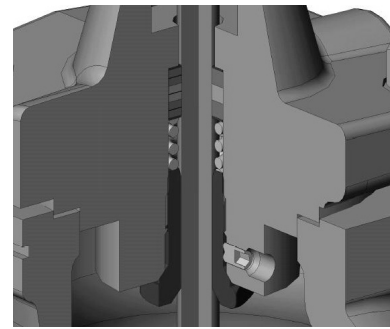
· Detail: Zirkulationssperre mit Gewindestift
